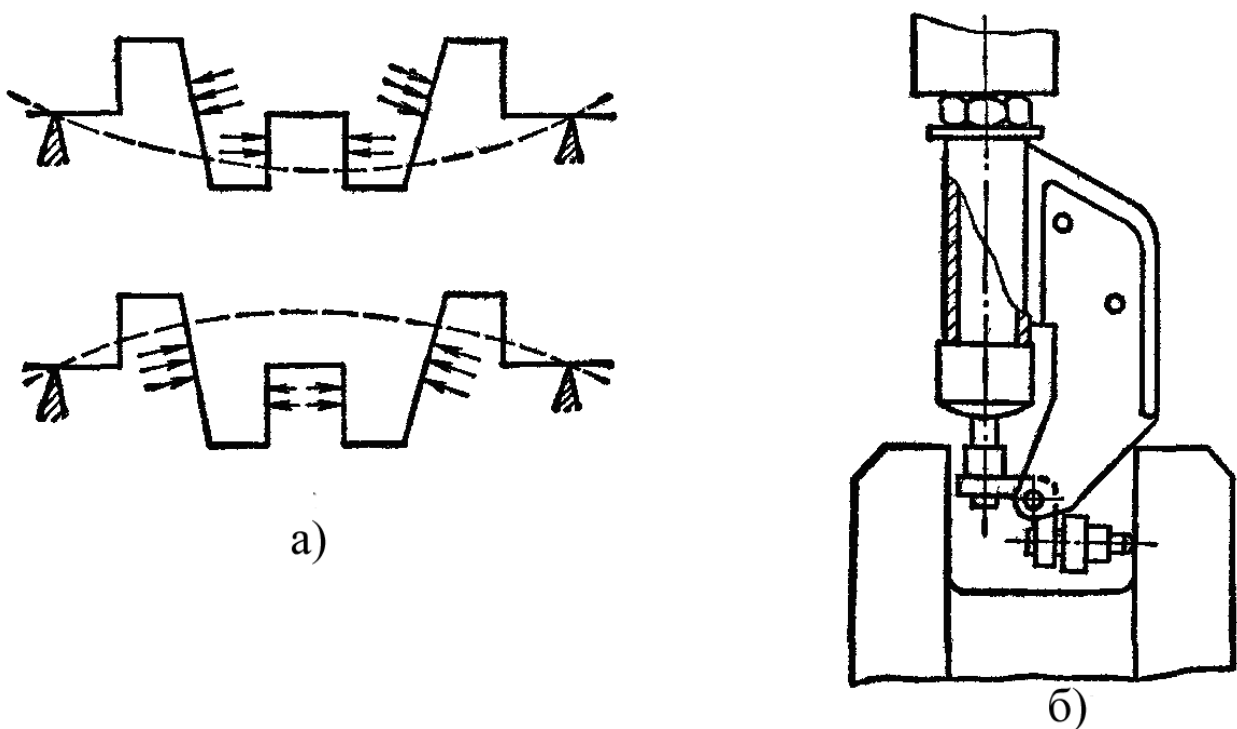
Схема наклепування (а); і пристрій (б) для виправлення колінчастого вала
